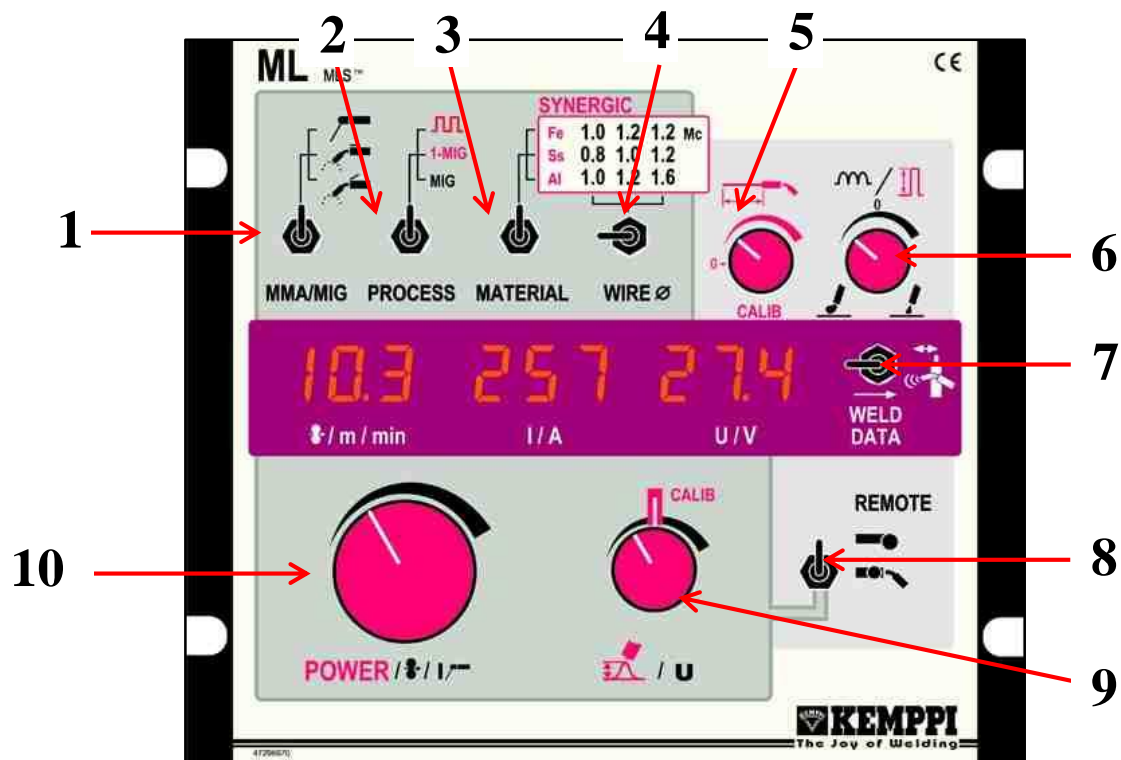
PANEL DE CONTROL FUENTE DE SOLDADURA KEMPPÍ
